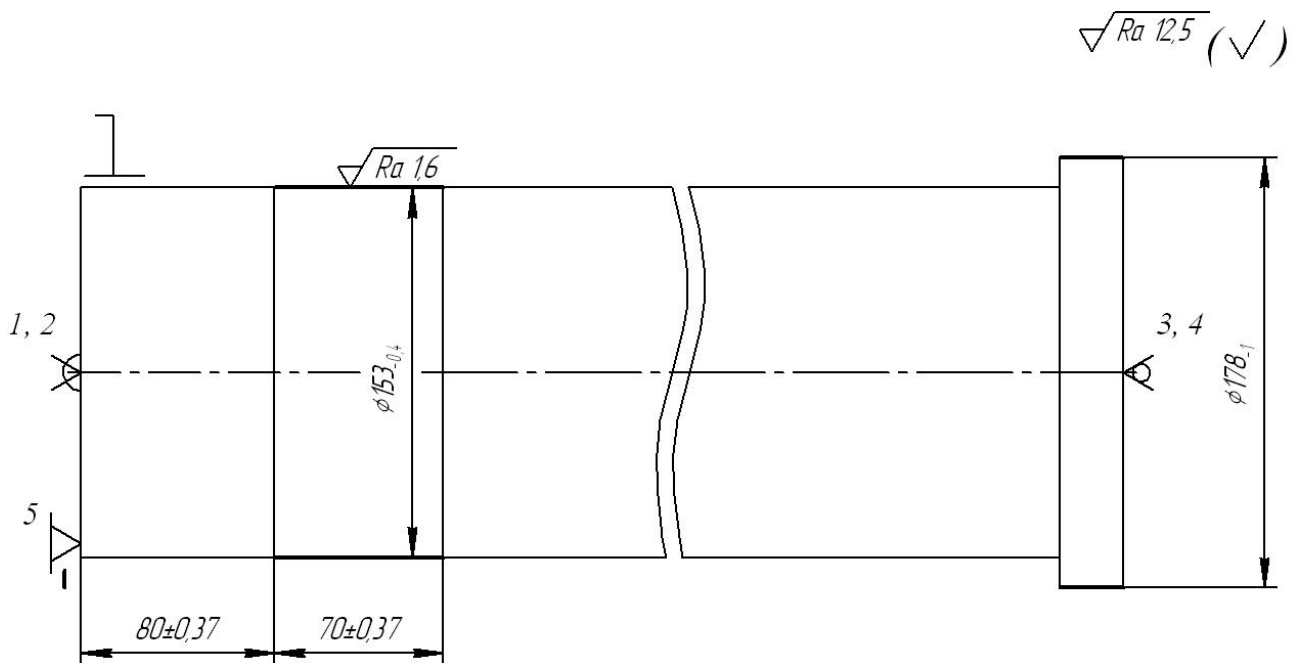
Схема базування заготовки на операції токарно-гвинторізній 020,
